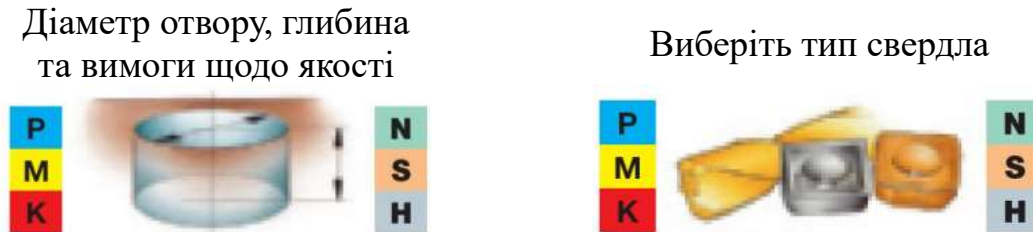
Вибір типу свердла за каталогом Sandvik
